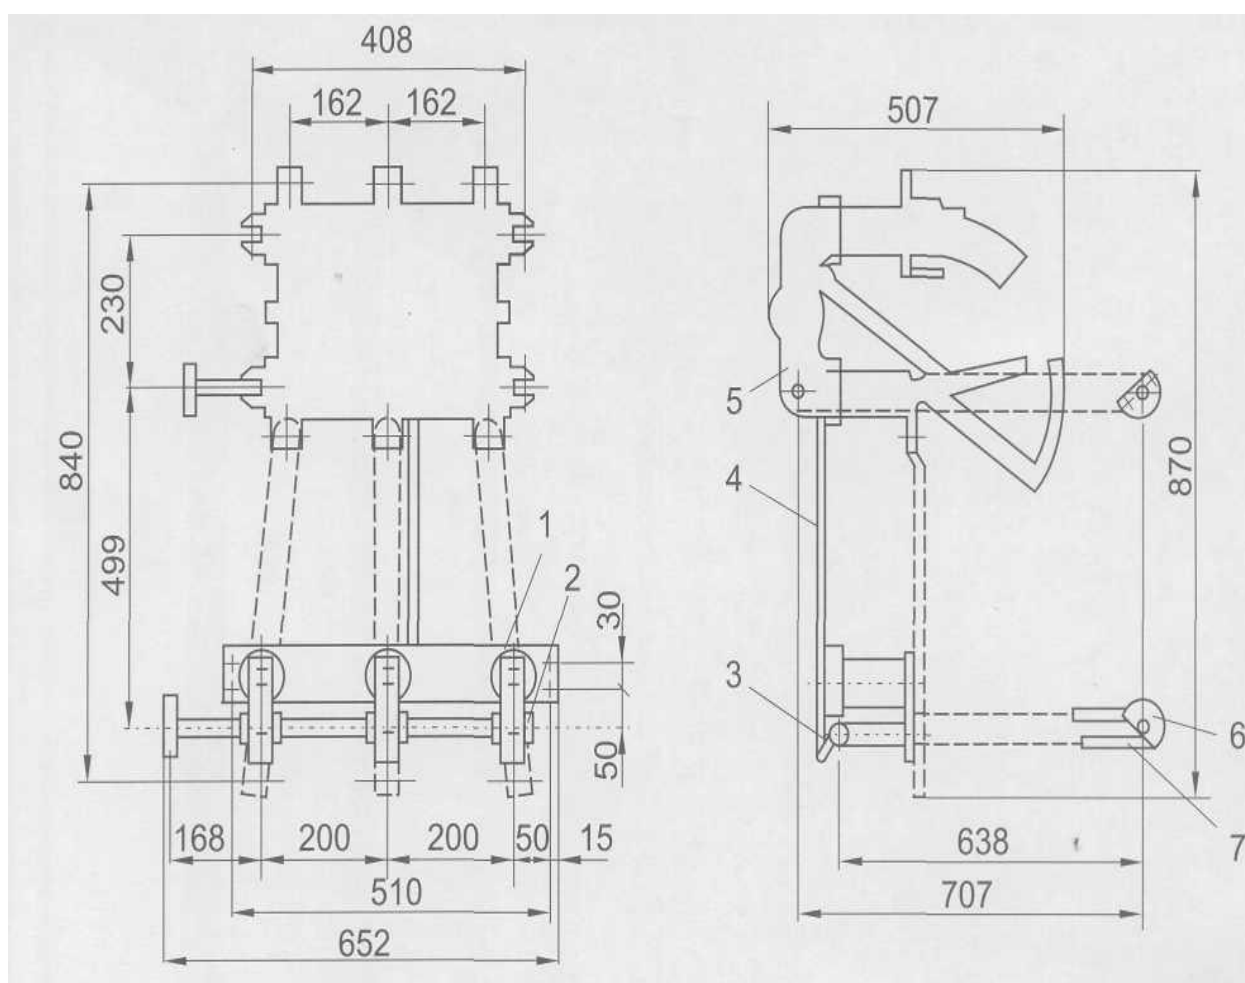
Габаритные, установочные и присоединительные размеры выключателя нагрузки ВНР-10/630-20 У2 (ТЗ). Масса 24,2 Кг
